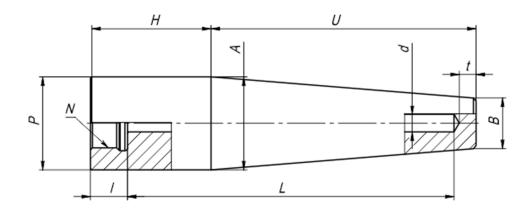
Гильза под приварку в стенку трубопровода (Weld-in), цельноточёная, коническая, под подвижный штуцер.
